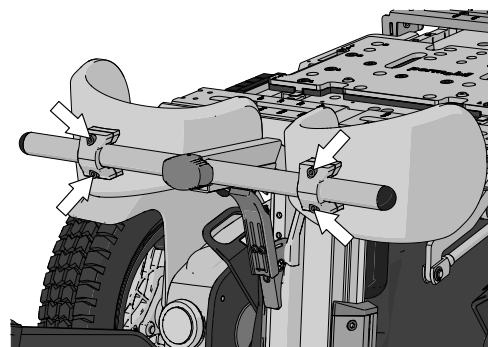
Auf jeder Halterung sind zwei Schrauben.
